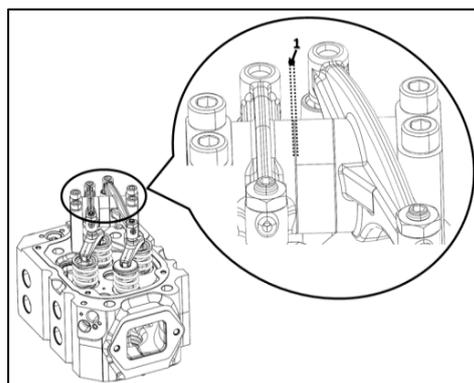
Г Проверка зазоров оси коромысел
